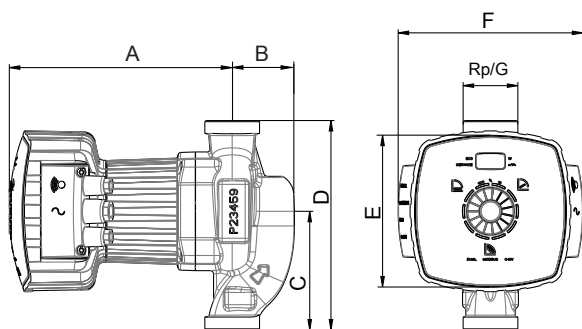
Pumpenaggregat mit Gewindeanschluss
